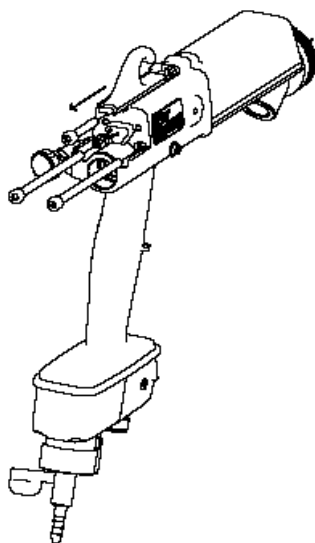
Demontaż przewodu doprowadzenia materiału do spustu pistoletu
